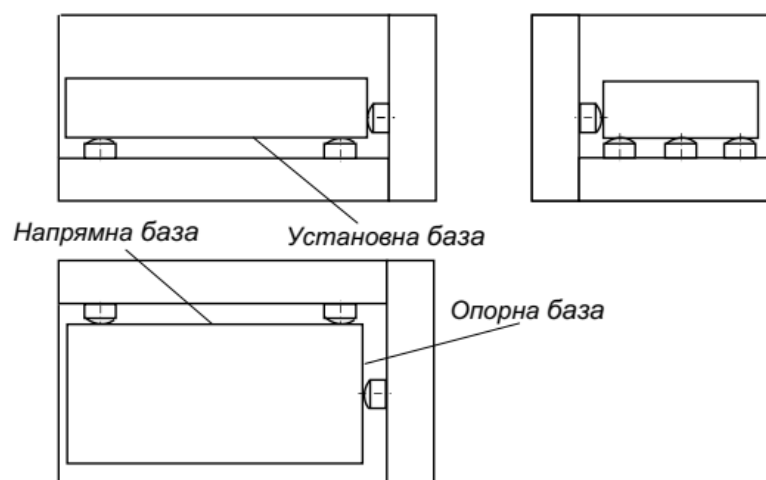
Приклад використання установної, напрямної та опорної баз для встановлення призматичної заготовки у верстатному пристрої
